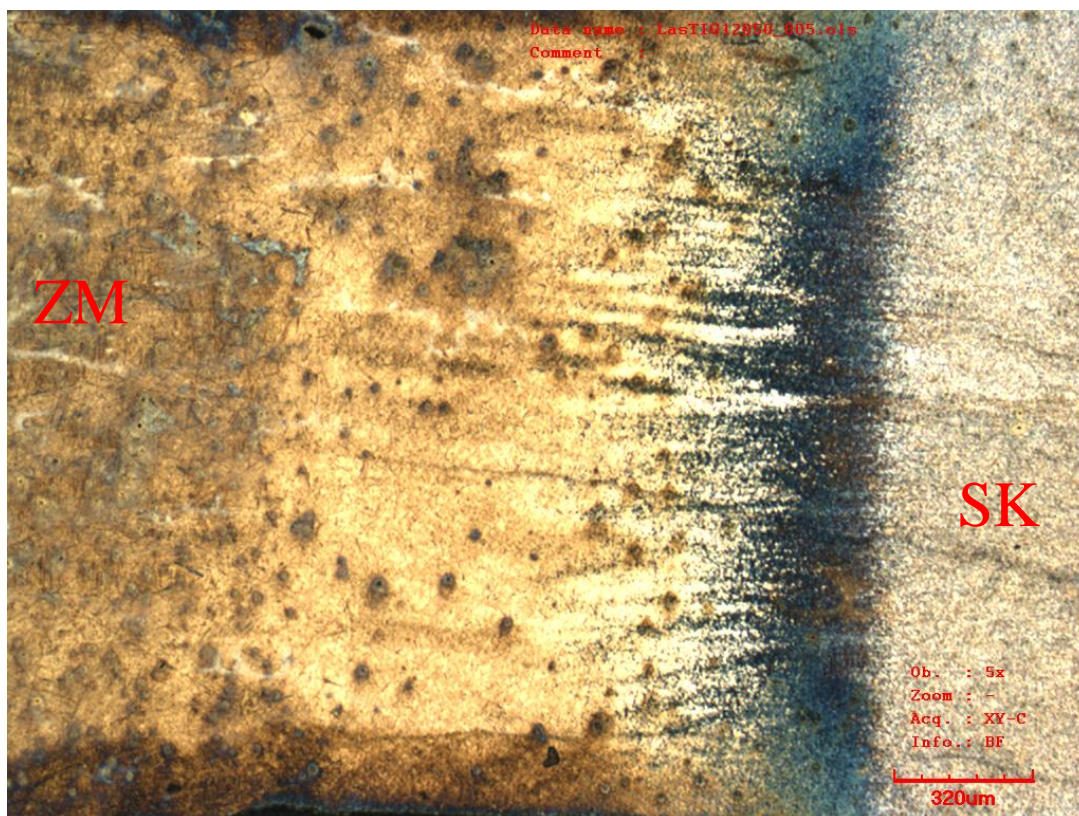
Mikrostruktura svarového kovu – laser 1000 W TIG 80 A DC
